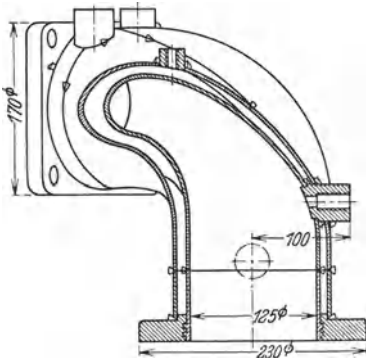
Geschweißter Auspuffstutzen einer Dieselmachine.
